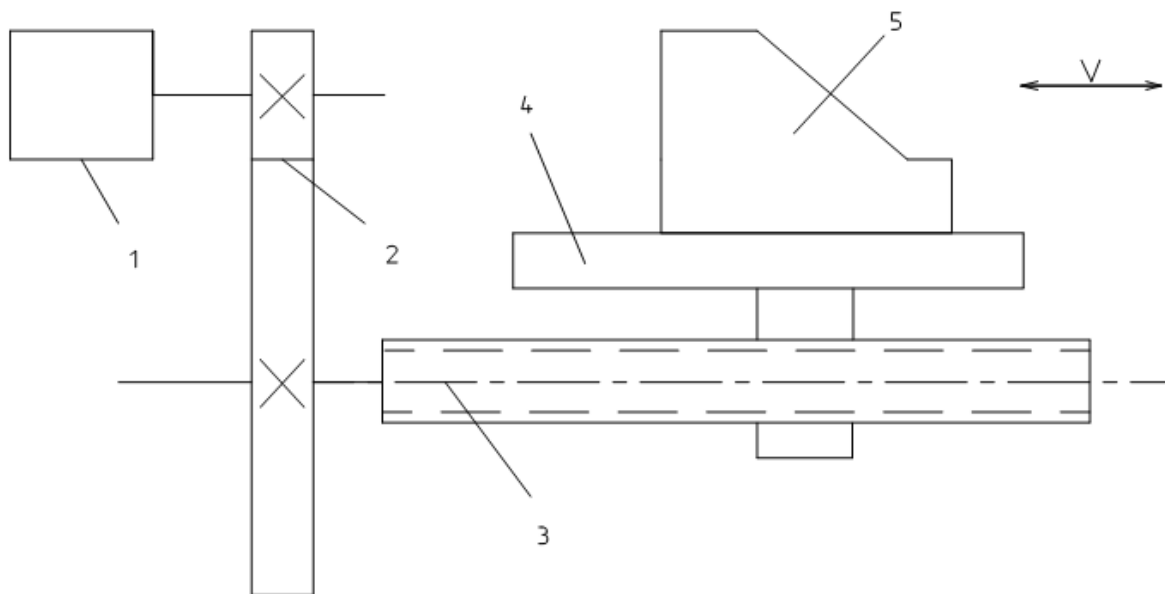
Типовая схема механизма привода подачи или вспомогательных перемещений: 1 – двигатель, 2 – редуктор (зубчатая или ременная передачи), 3 – винтовая передача; 4 – рабочий орган станка; 5 – деталь
